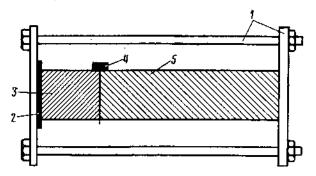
Прижим, используемый при пайке стыковых соединений составного режущего инструмента: 1— прижим из нихрома, 2— слюдяная прокладка, 3— твердосплавная пластия», 4— медный припой, 5— стальная державка
